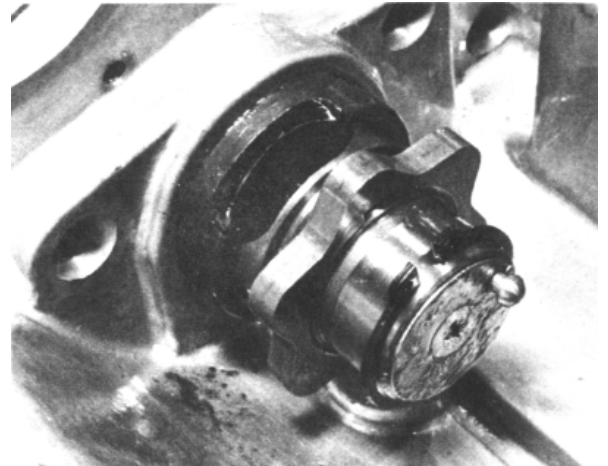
die Nockenscheibe sowie den Sicherungsring wieder einbringen
